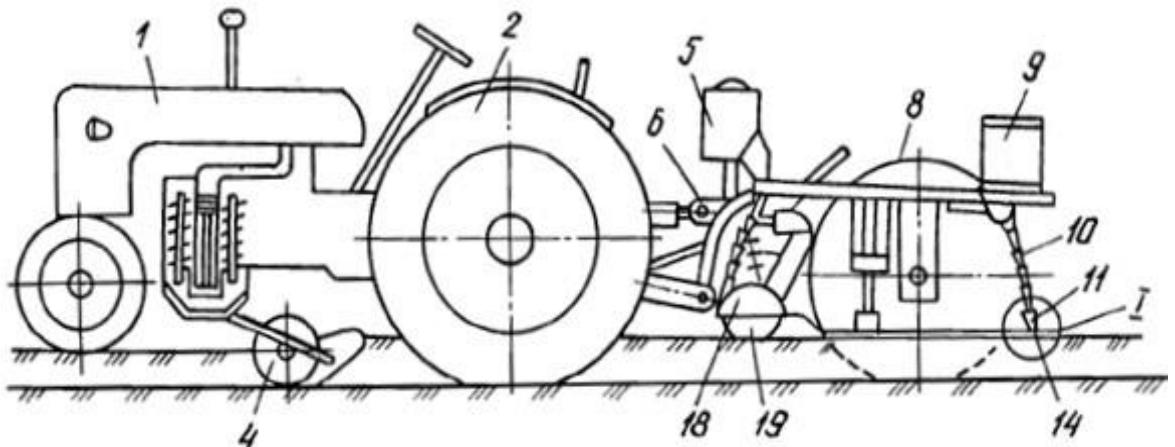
Грядоделатель-сеялка: 1-трактор; 2, 3 – ведущие колеса; 4- борооздообразователь; 5-туковысыевающие аппараты; 6-навеска; 7, 8- формирующие колеса; 9-сеялка; 10-семяпровод; 11-раструбы; 12-Г-образные пластины; 13-щиток, 14-наральник; 15-хвостовики; 16-вертикальные стенки; 17-полки; 18-кожух; 19-фреза; 20-задняя стенка; 21-вертикальная стенка; 22- гидроахимной механизм; 23-ось; 24-винт; 25-дугообразные пазы;
